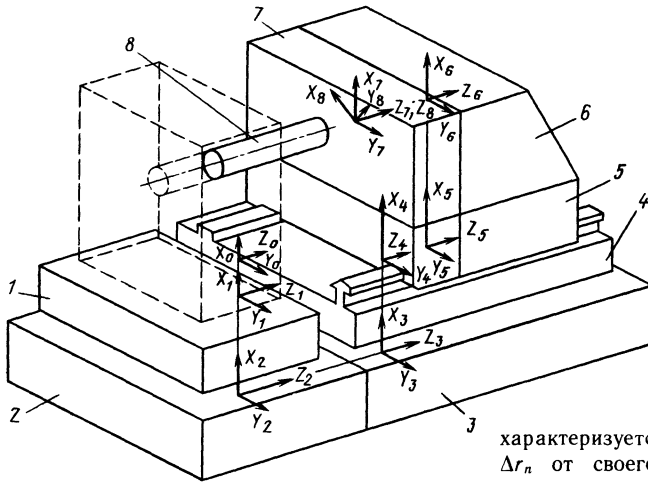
Формирование суммарной погрешности агрегатно-расточного станка: 1— приспособление; 2— боковая станина; 3— центральная станина; 4— направляющая плита; 5— подвижная платформа; 6— упорный угольник; 7— инструментальная бабка; 8— шпиндель
